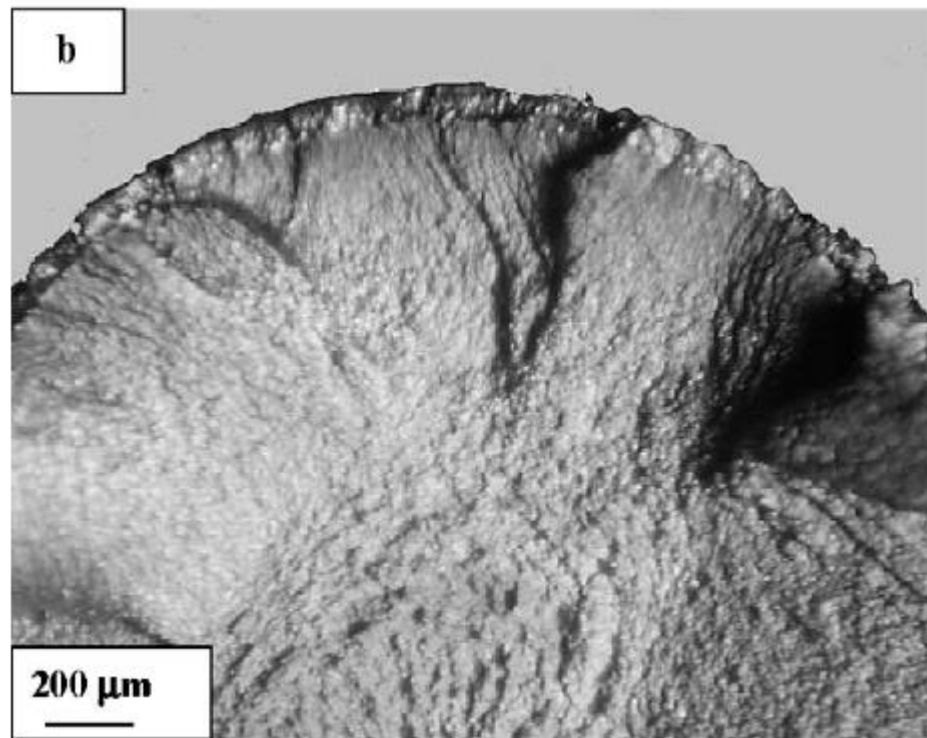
Grietas originadas desde el recubrimiento de cromo hasta el sustrato
